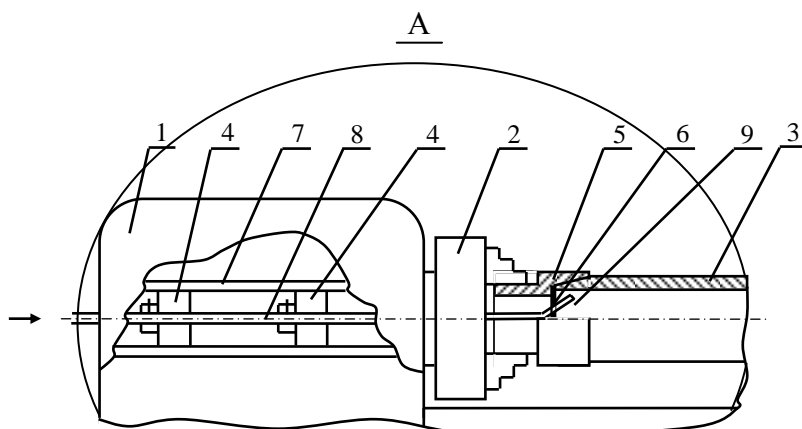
Схема переднего приспособления для вращения и подачи краски на внутреннюю поверхность труб.1-установка для закрепления и вращения труб; 2- патрон установки;3-труба; 4- текстолитовые подшипники; 5-держатель трубы; 6-резиновая прокладка; 7-шпindelь установки; 8-труба для подачи краски; 9-головка для напыления краски.
